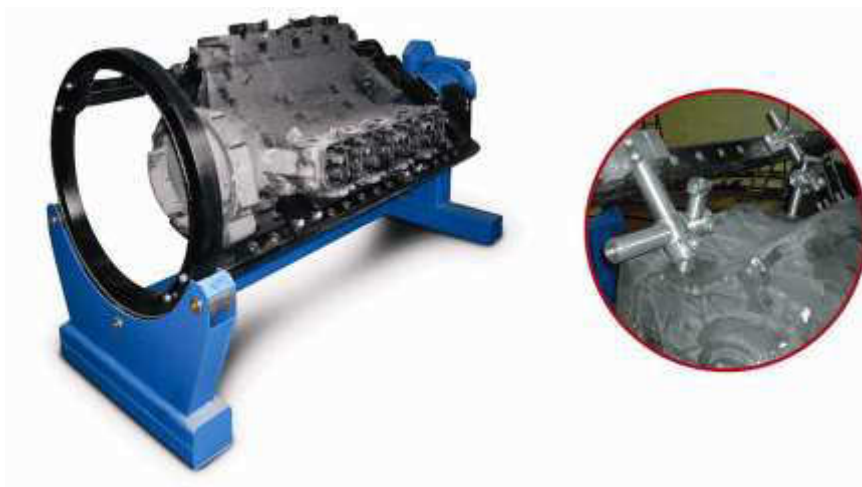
Стенд универсальный для разборки-сборки двигателей P776E
